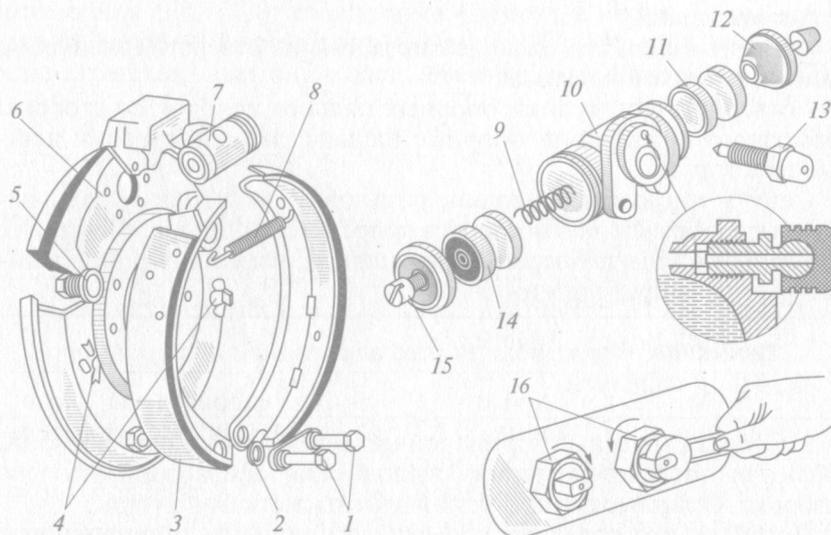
Колесный тормозной механизм автомобиля ГАЗ-53А:
